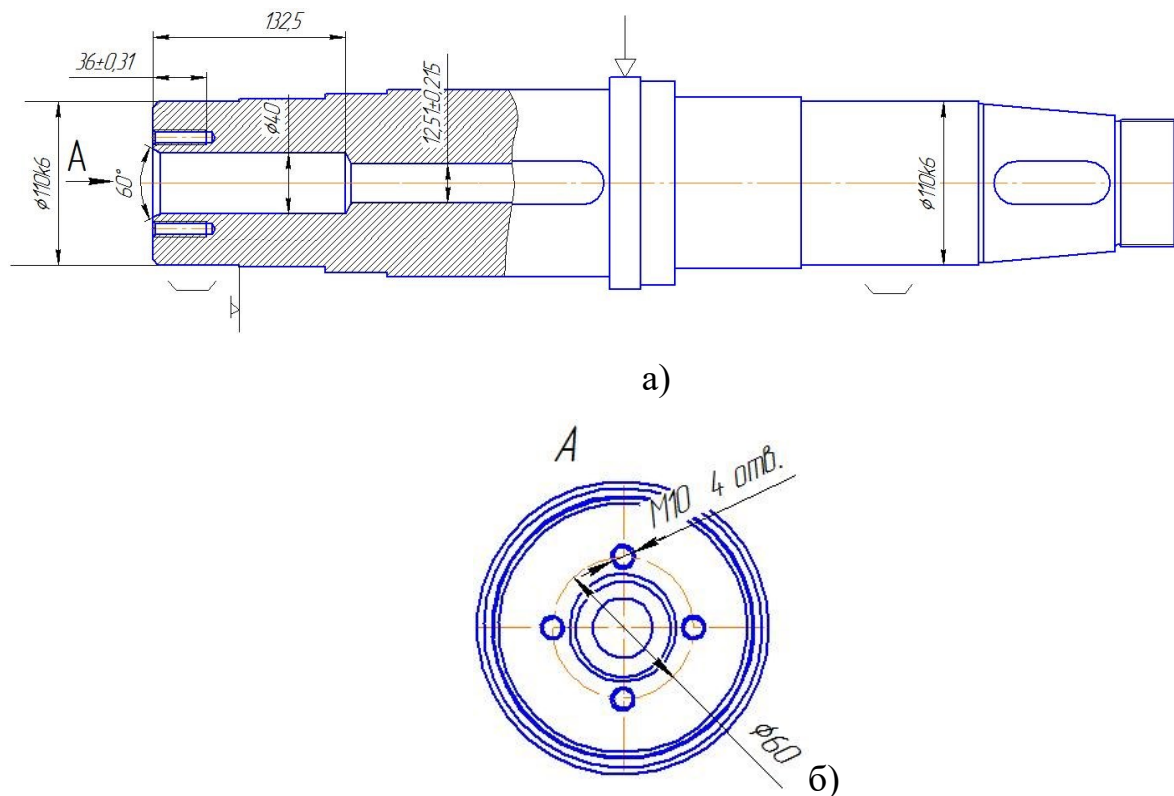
Базування, закріплення заготовки і поверхні, що обробляються
